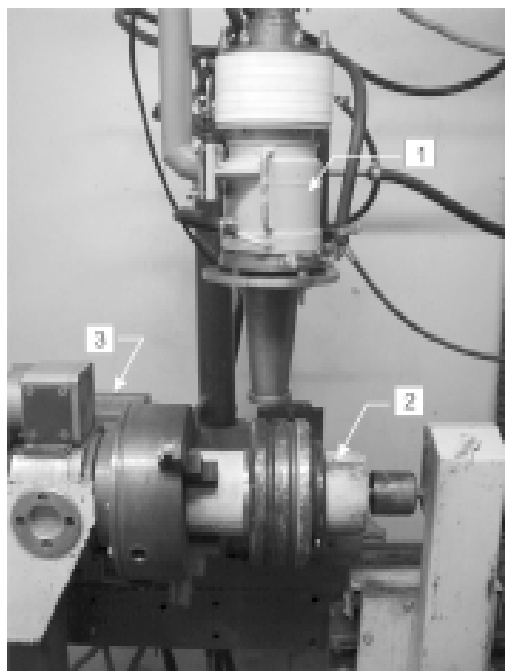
Вид установки для упрочняющей обработки прокатных шайб.
